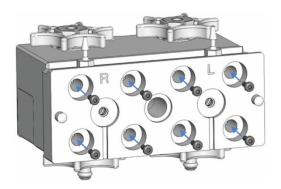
Pumpenkopf mit Hinterspülplatte und Schrauben für die Platte
